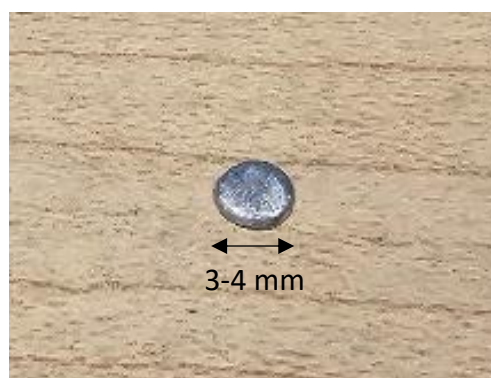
Échantillon de soudure pour analyse DSC
